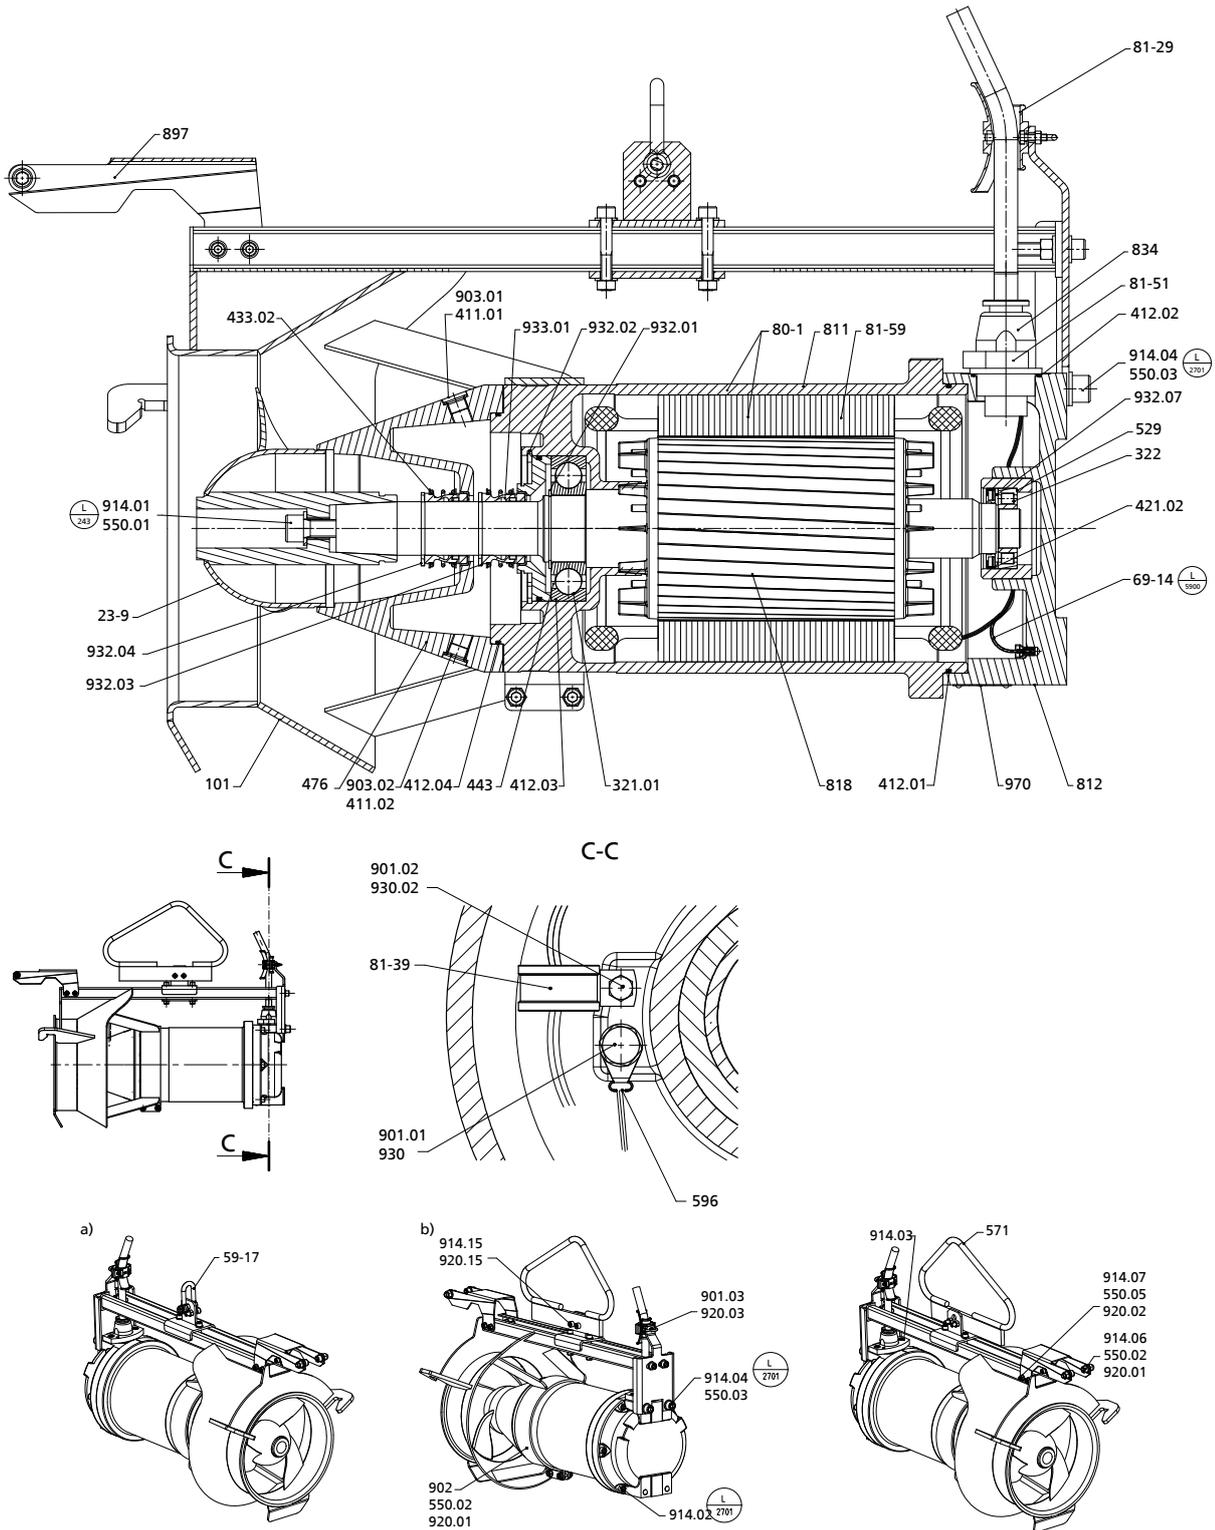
Чертеж общего вида: а) с серьгой б) со скобой (дополнительно)
